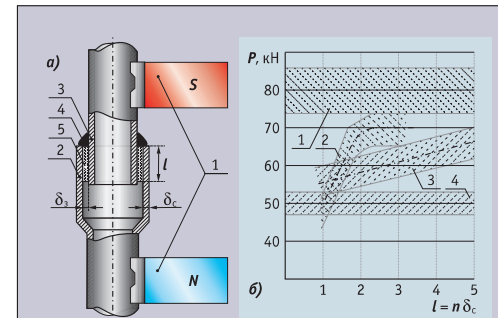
Схема (а) и графики прочностного поведения (б) соединений, выполненных магнитной пайкой: а) 1 — магниты; 2 — раструб («стаканчик»); 3 — труба; 4 — припой; 5 — железный порошок; δ_3 — толщина стенки трубы (раструба); δ_3 — зазор. б) области разрушения: 1 — материала трубы; 2 — паяного соединения при $\delta_3 = 0,5$ мм; 3 — паяного соединения при $\delta_3 = 1,0$ мм; 4 — резьбовых соединений; Р — разрушающая нагрузка; l — длина паяного соединения; n — число, кратное отношению длины паяного соединения к толщине стенки трубы (раструба)
